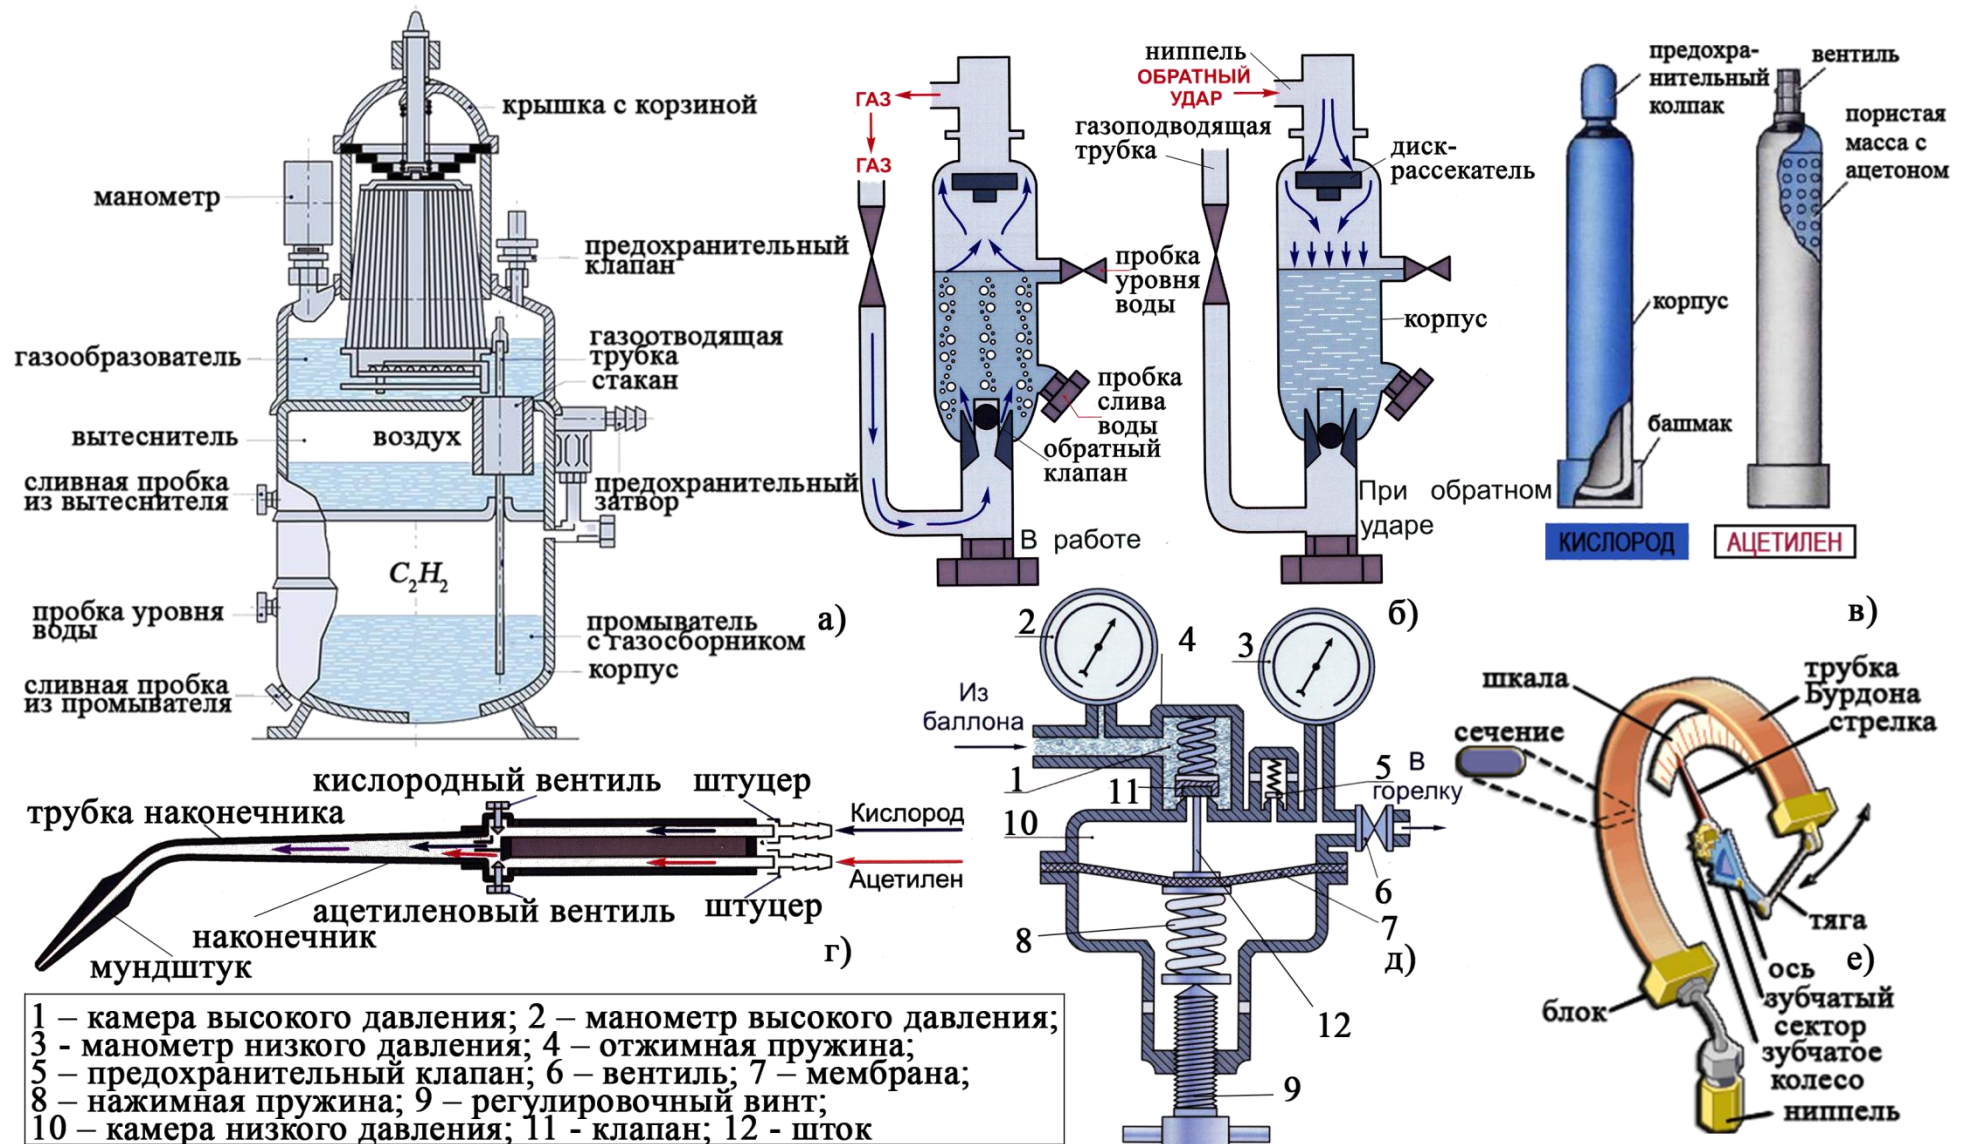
Оборудование для газовой сварки: а) ацетиленовый генератор; б) предохранительный затвор; в) газовые баллоны; г) ацетиленовая безинжекционная горелка; д) редуктор; е) манометр
